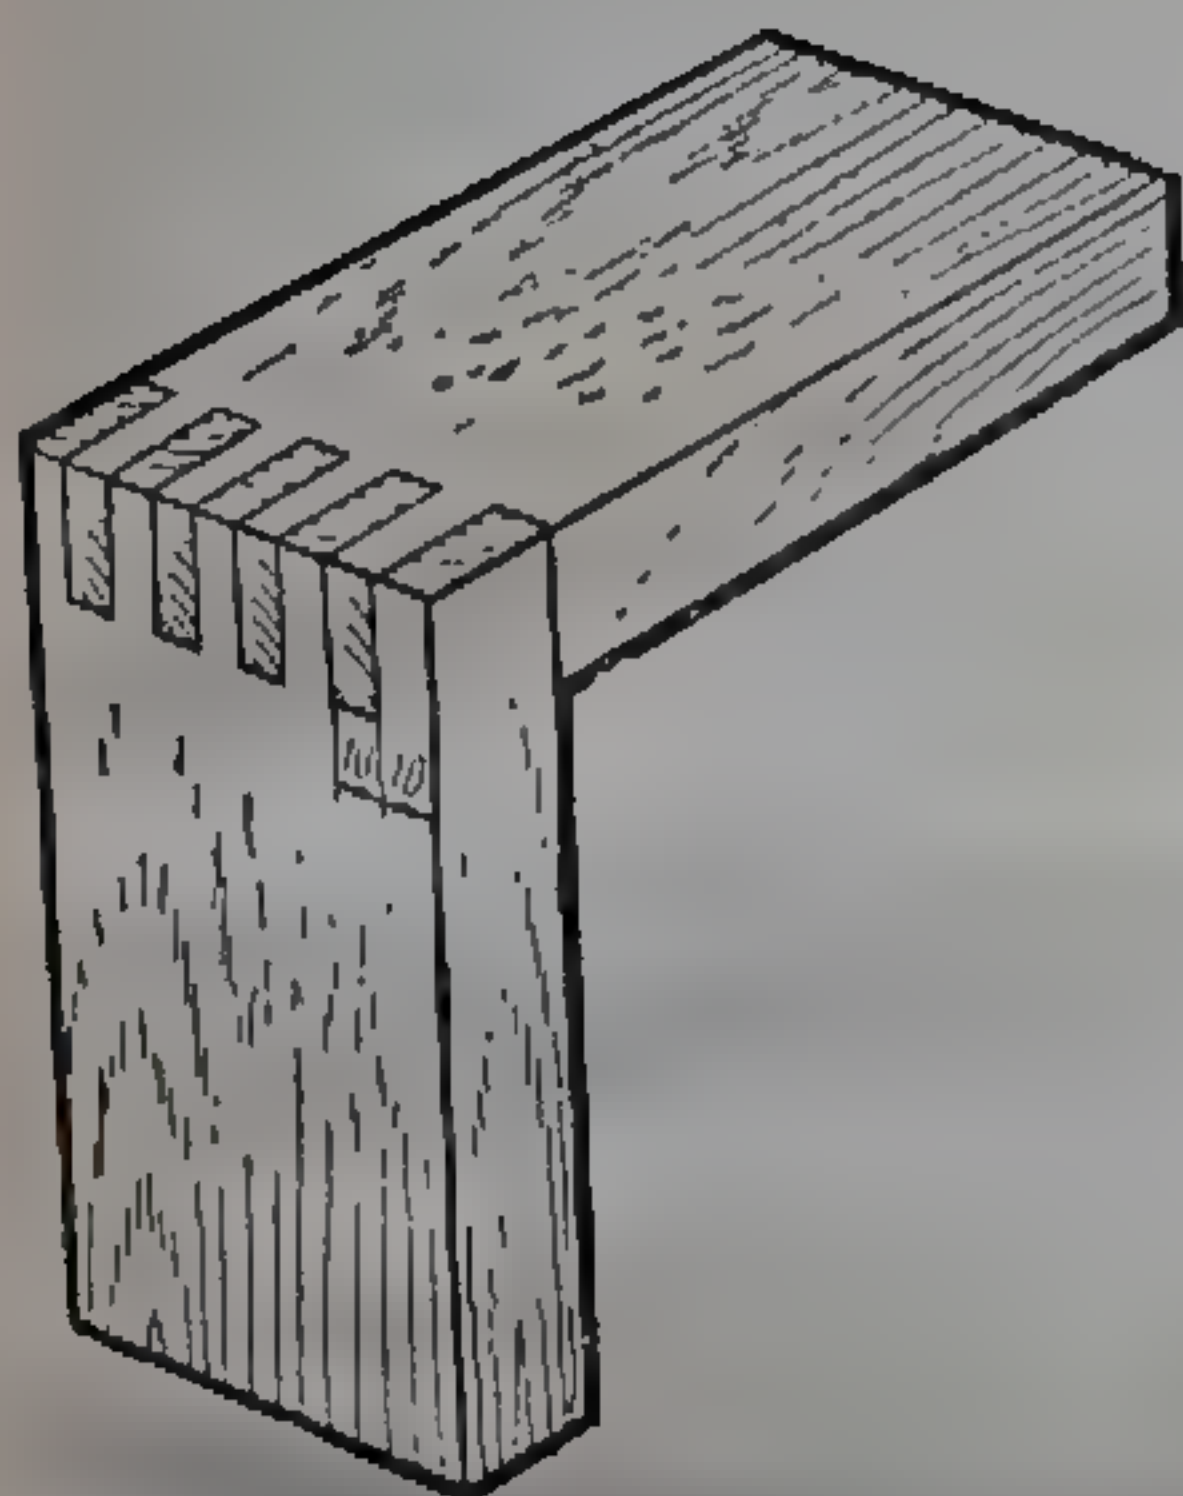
Чертеж ящичного соединения на шип прямой открытый УЯ-1.
